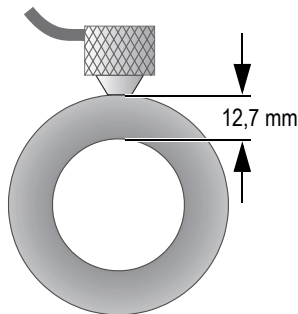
Acoplamento de um transdutor de elemento duplo
